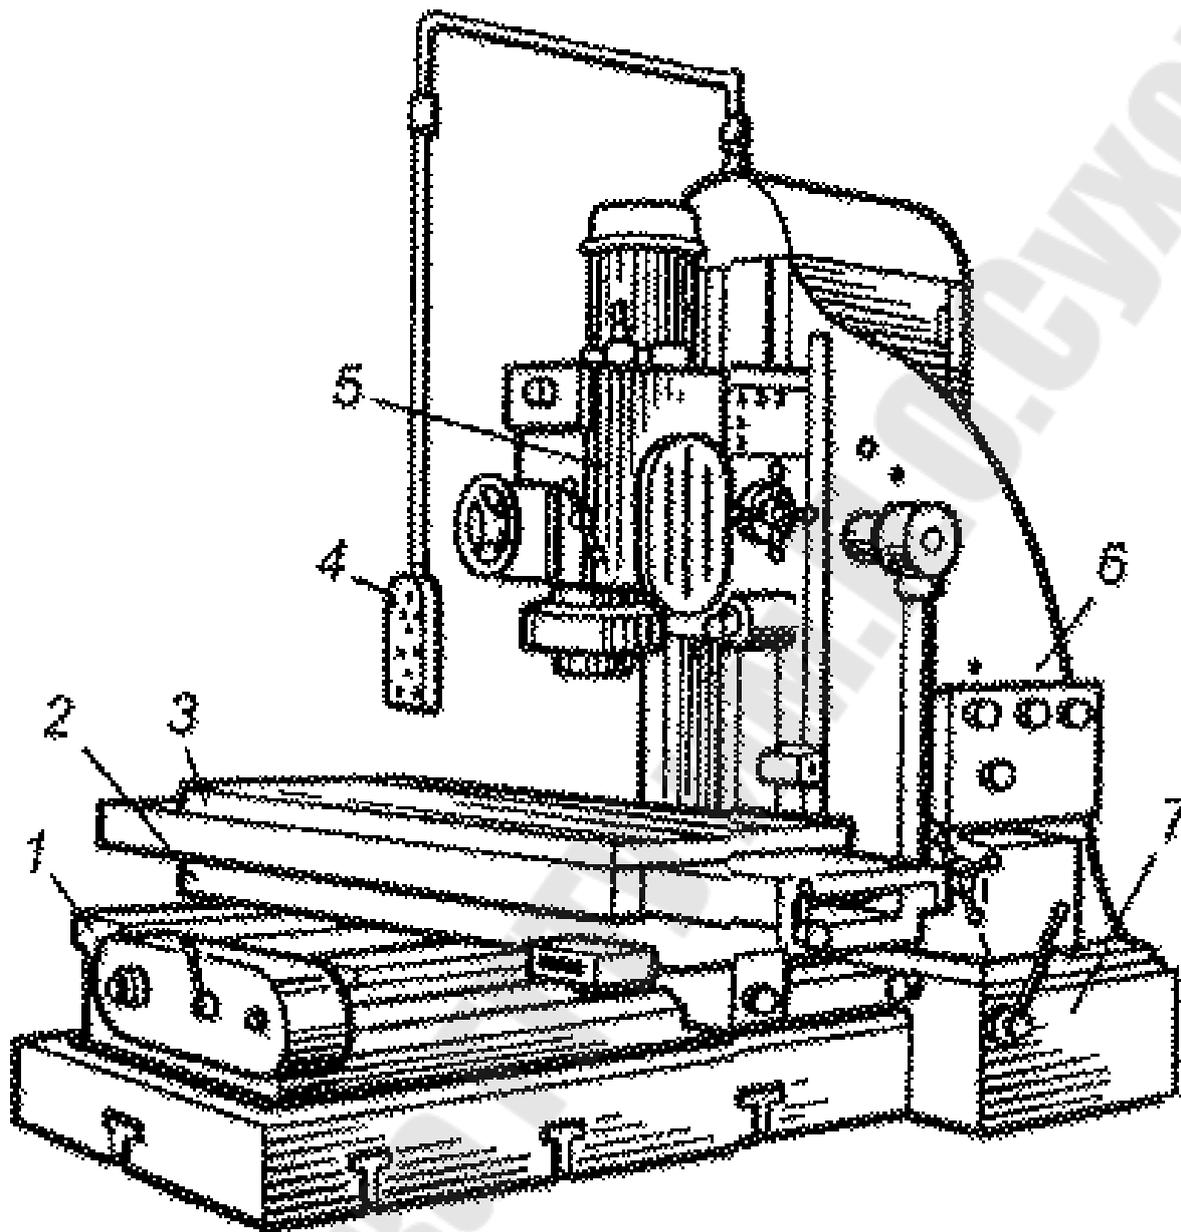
Общий вид бесконсольного вертикально-фрезерного станка
